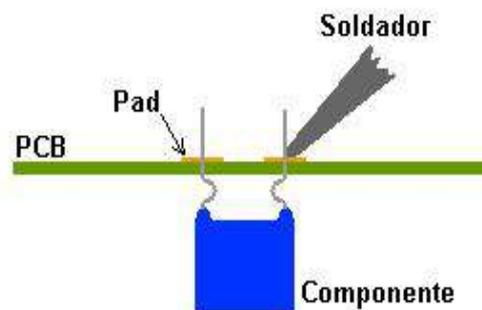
Fig. N. : Vista de área de trabajo de una plaqueta de circuito impreso, el herramental, y la colocación y soldadura de un componente discreto.
